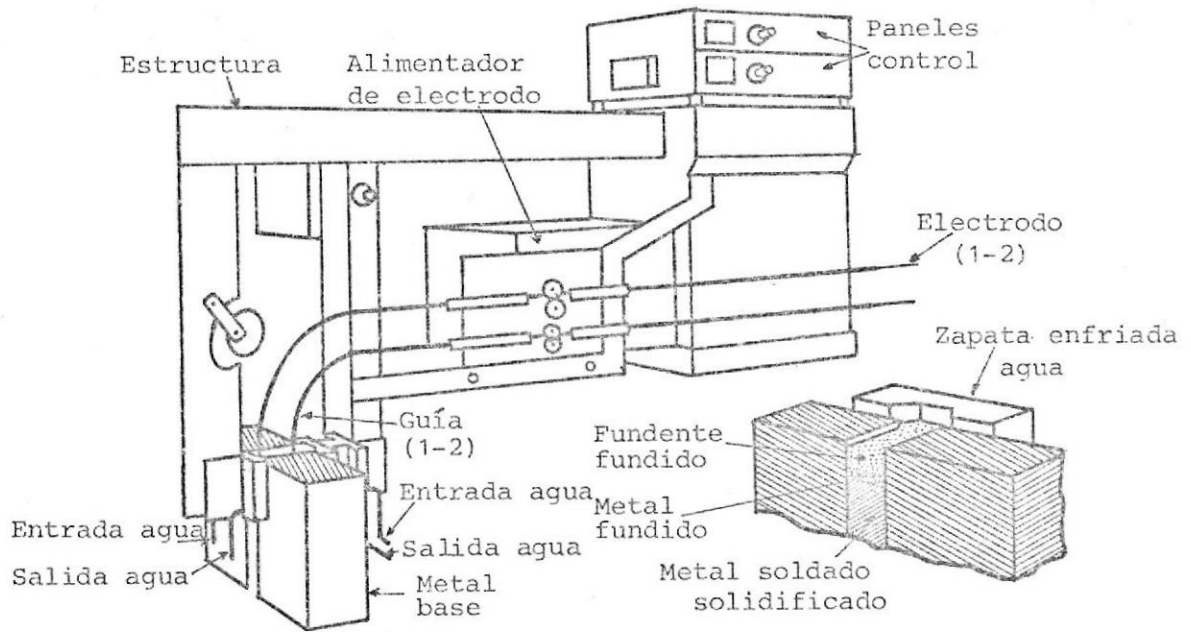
Componentes principales del equipo convencional para soldadura por electroescoria usando guía no consumible (Ref. 1).
